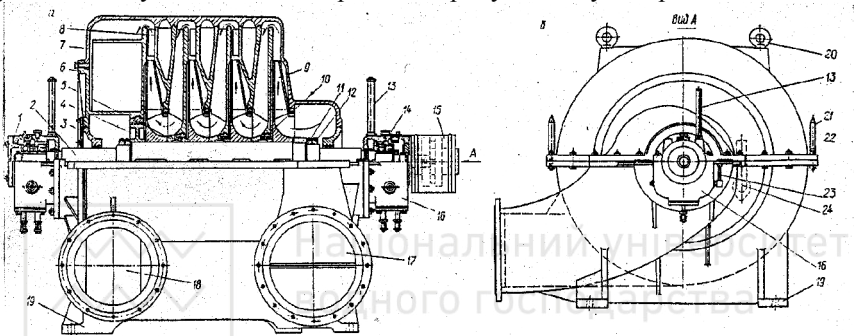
Повітродувка (тип ТВ) - а) поздовжній переріз ; б) вигляд з боку всмоктувального патрубку: 1- корпус радіально-упорного підшипника; 2- вал; 3- кінцеве ущільнення; 4- розвантажувальна п'ята; 5- дистанційна втулка; 6-кришка; 7- корпус; 8- діафрагма; 9- робоче колесо; 10- ущільнення; 11- гайка; 12- контргайка; 13- чохол термометра; 14- радіальний підшипник; 15- огороження муфти; 16- масляна ванна; 17- всмоктувальний патрубок; 18- нагнітальний патрубок; 19- опорні лапи; 20- рим-болт; 21- напрямляюча колонка; 22- установочний гвинт; 23- мастилопоказчик; 24- розвантажувальна труба
